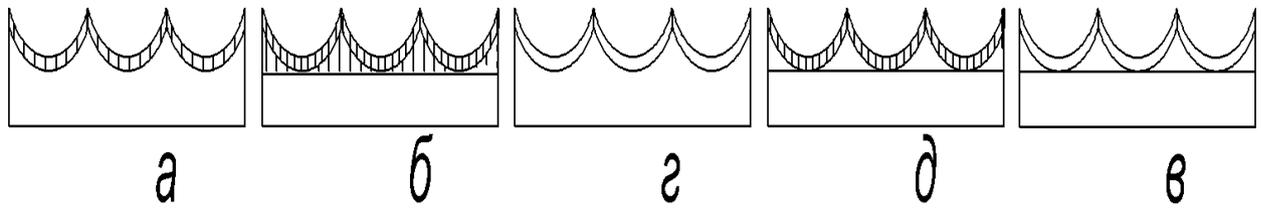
Види зубчастої ріжучої кромки ножів для хліборізок.
